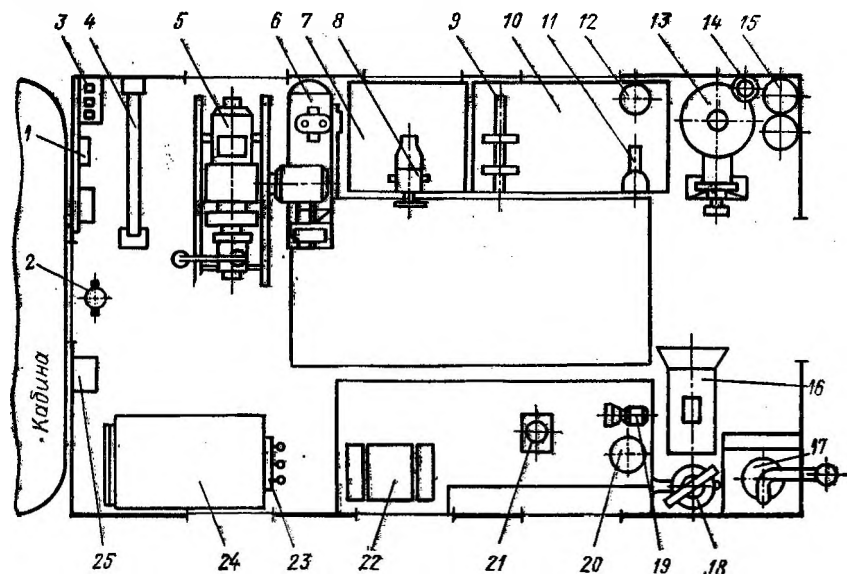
Схема размещения оборудования на ВАРЭМ-3:
